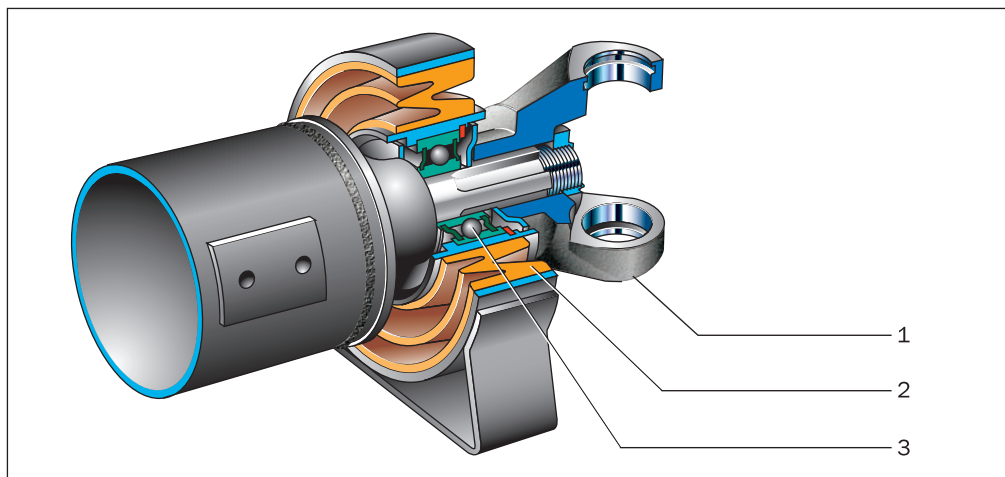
Конструкция промежуточной опоры: 1 — вилка; 2 — упругая подушка; 3 — подшипник промежуточной опоры
